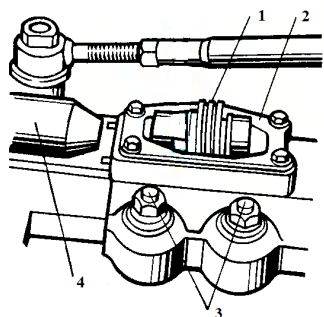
Регулировка колеи ведущих колес трактора: 1 – винт; 2 – прокладка; 3 – клинья; 4 – крышка (показана в снятом положении).
